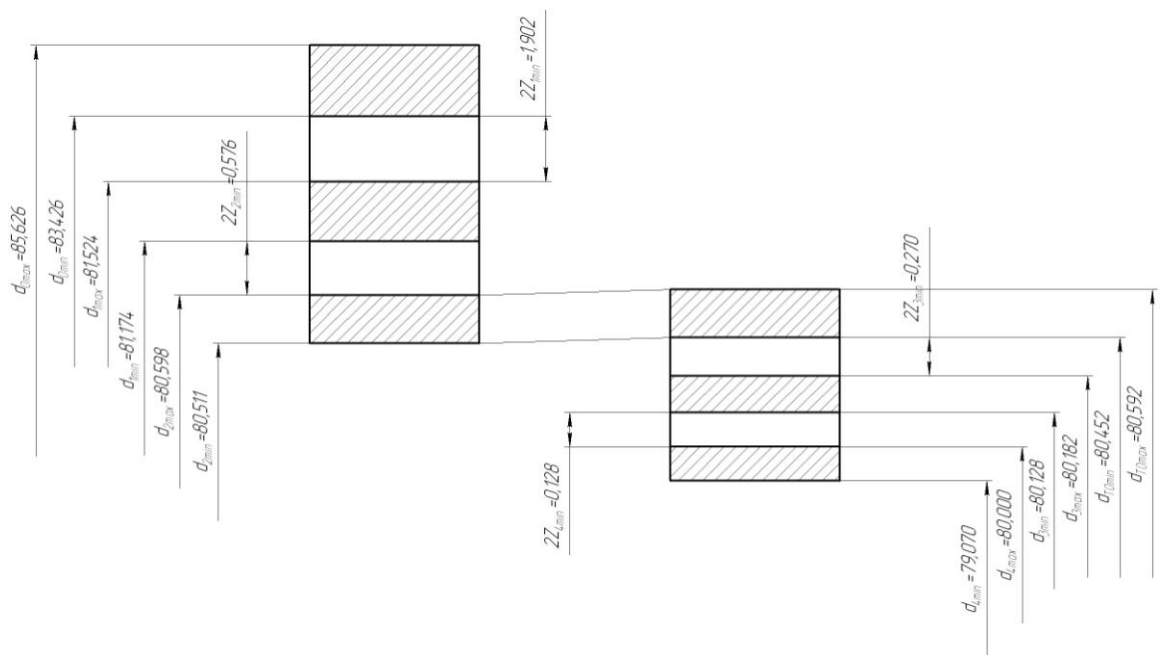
Схема расположения полей допусков и припусков.
